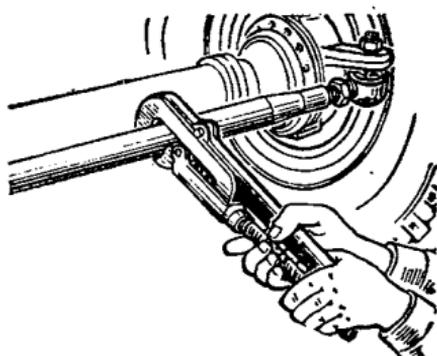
Регулировка схождения колес автомобиля УАЗ-469
